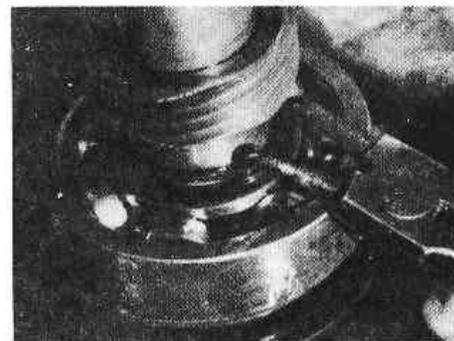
Снятие шестерни 3-ей передачи и синхронизатора — коробка передач типа С (Разд.6)
